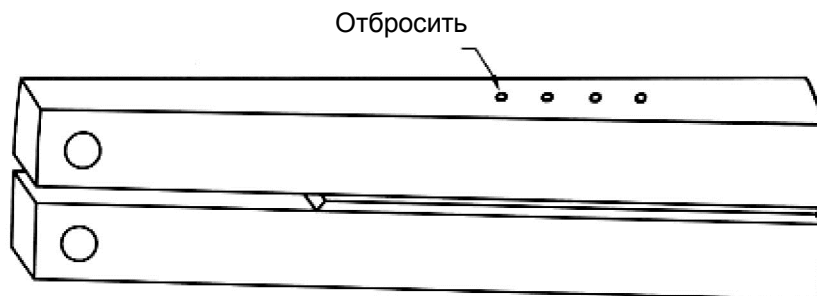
Расположение отпечатков индентора при измерении твердости на образце DCB
